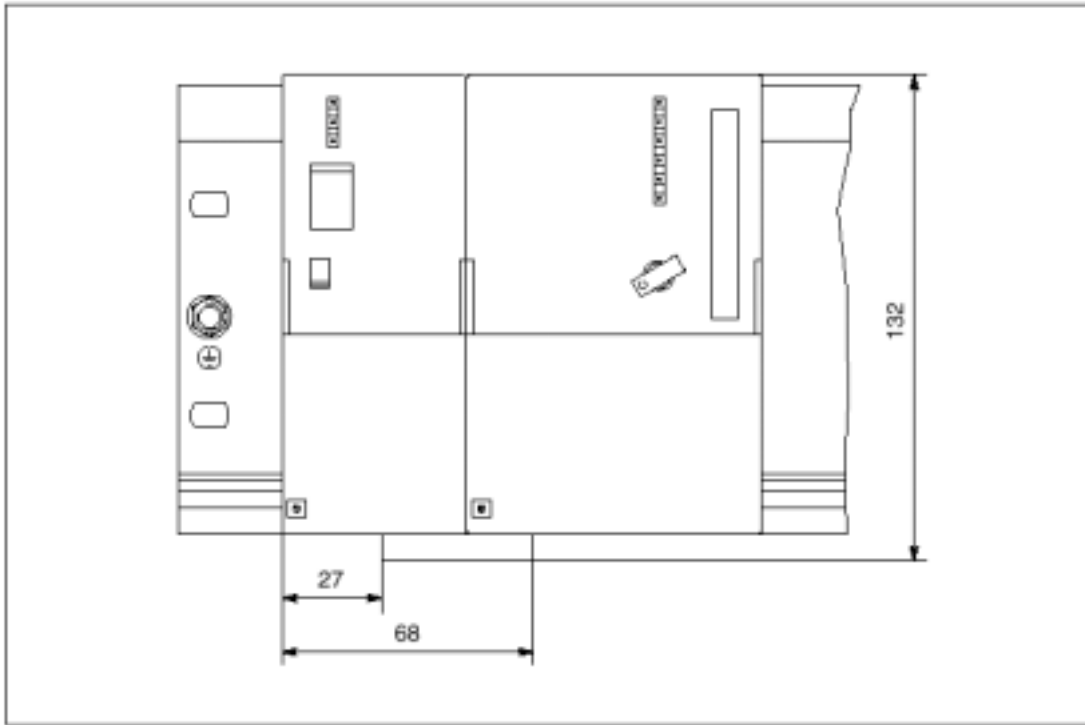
Чертеж с размерами блока питания 307; 5 А с CPU 313/314/315/315–2 DP. Вид спереди
